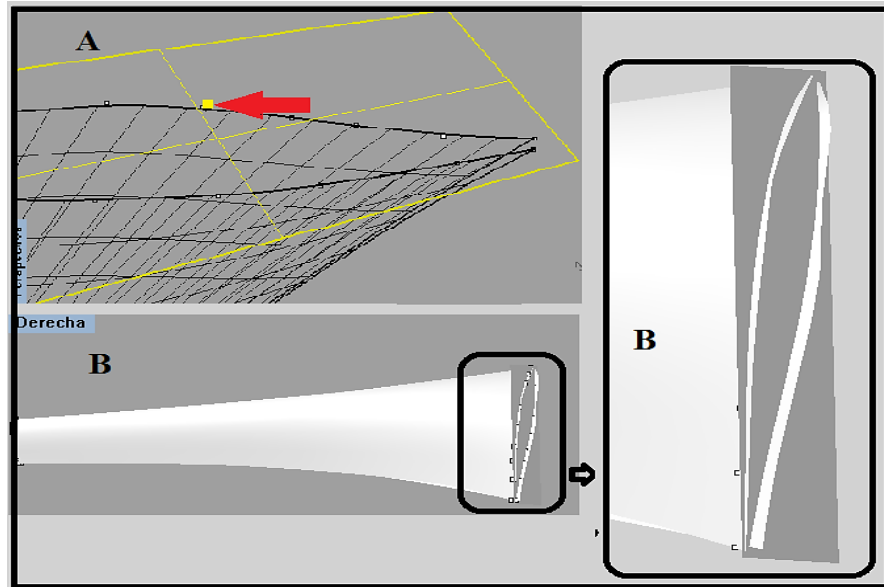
Movimentando os planos, A) O plano é movimentado até o ponto final e B) a superfície é estendida até que corte tudo o plano
